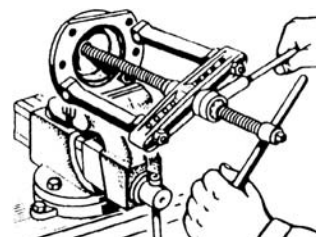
Выпрессовка внешней обоймы подшипника № 7610K1 из стакана вторичного вала.
